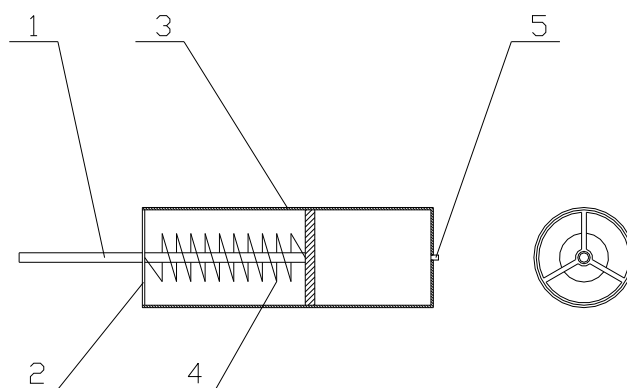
Схема пневмоцилиндра; 1-поршень, 2-крышка стакана, 3-стакан, 4-АЭ, 5 - клапан.
